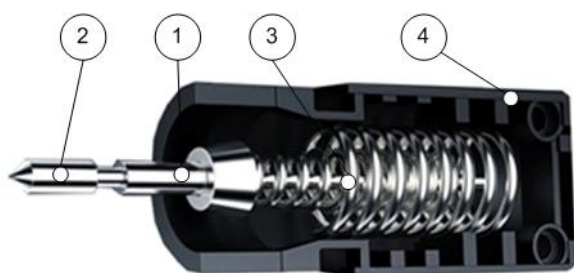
Механизм стеклобоя нажимного типа: 1- металлический стержень; 2 – боёк; 3 – пружины; 4 - корпус
